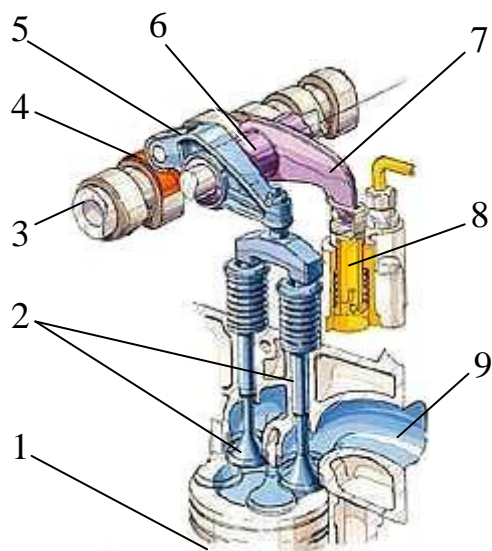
Конструкция газораспределительного механизма двигателя грузового автомобиля с декомпрессионным моторным тормозом: 1 – поршень двигателя; 2 – выпускные клапаны; 3 – распределительный вал; 4 – дополнительный кулачок; 5 – коромысло привода выпускных клапанов; 6 – соединительный вал; 7 – управляющий рычаг; 8 – гидроцилиндр; 9 – выпускной канал
